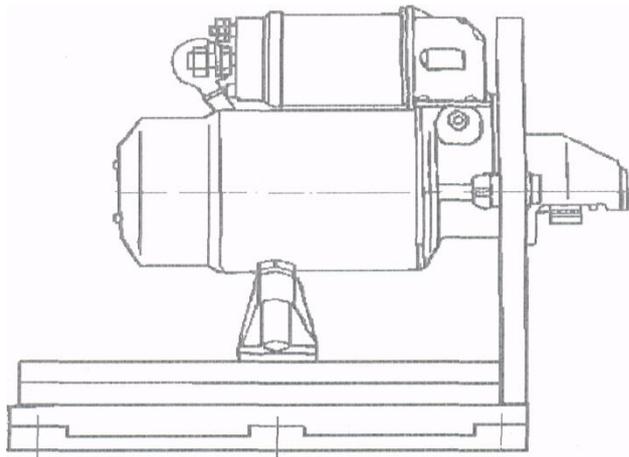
Установка стартера за фланец на столе нагрузочного устройства.
